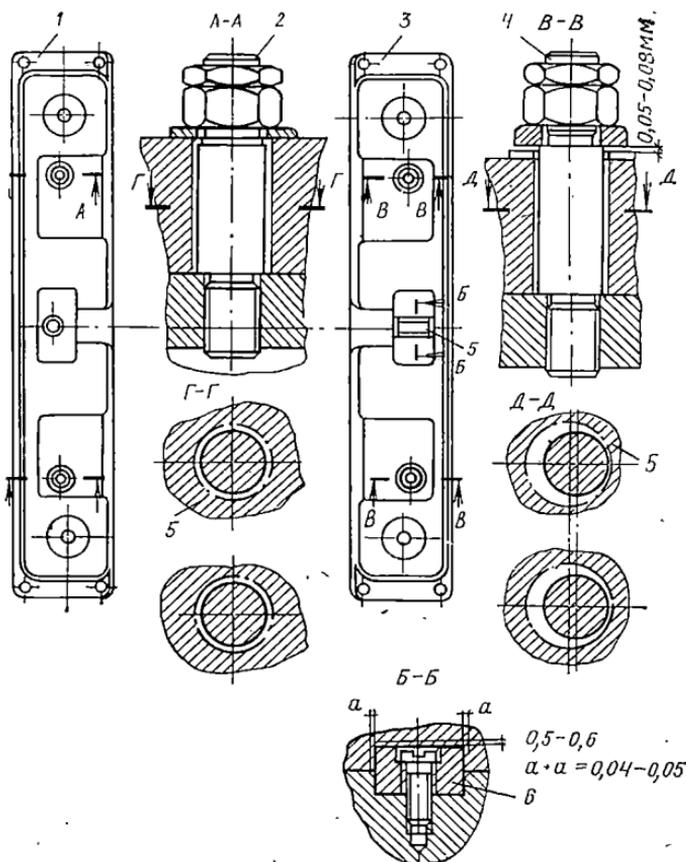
Положение шпилек крепления подвижного и неподвижного подшипников к опорным плитам
